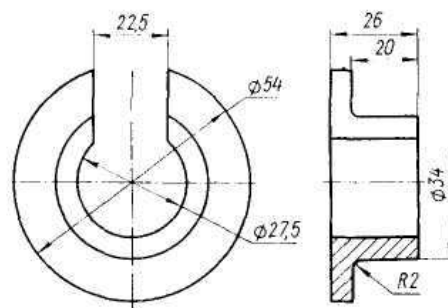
Оправка для спрессовки подшипникового узла с полуоси
